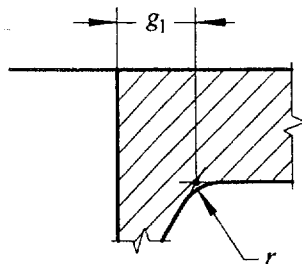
Brides à collerette soudée en bout ou monobloc avec l'enveloppe cylindrique
